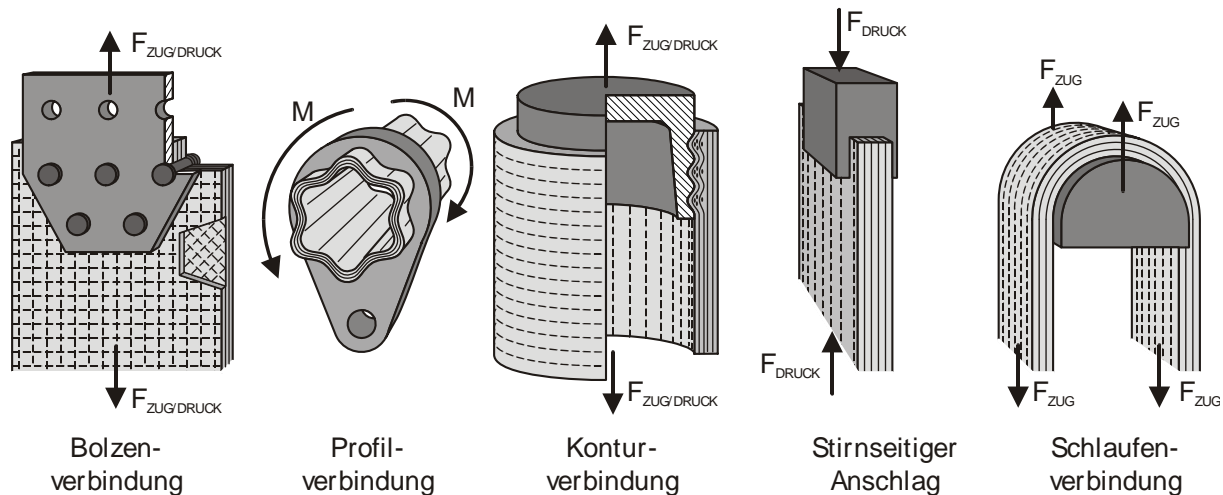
Bewährte formschlüssige Prinzipien zur Lasteinleitung bei FKV-Strukturen
